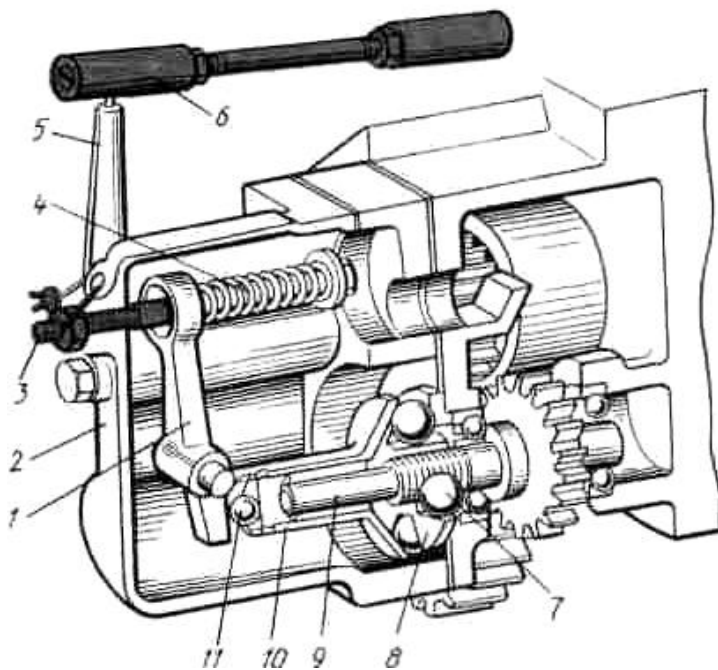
Шариковый регулятор пускового двигателя П-10УД:
